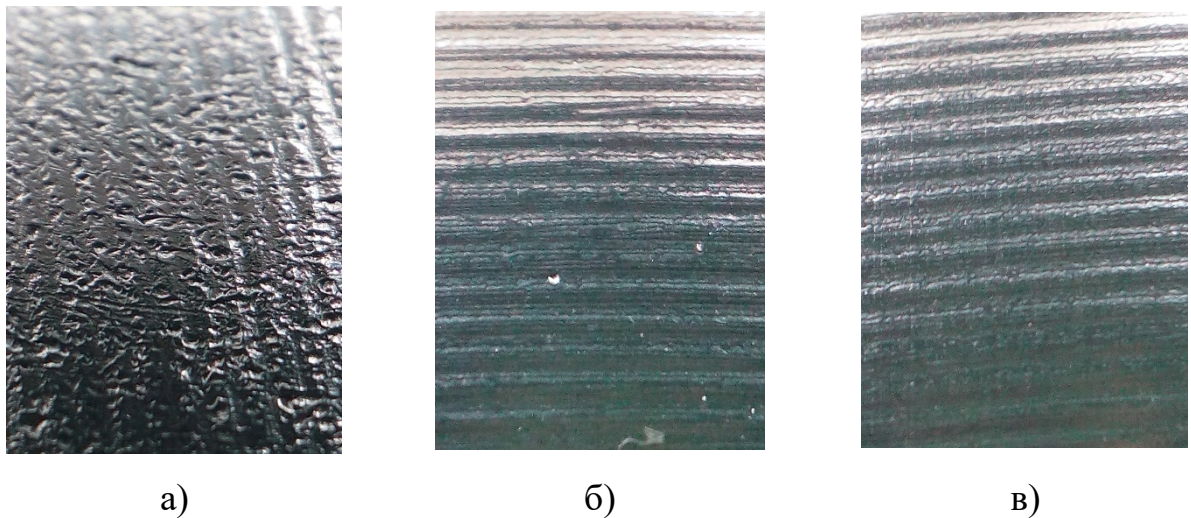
Зовнішній вигляд попередньо фрезерованої поверхні деталі після МАО порошком Полімам - М (400/315 мкм) з різною величиною робочого зазору:
